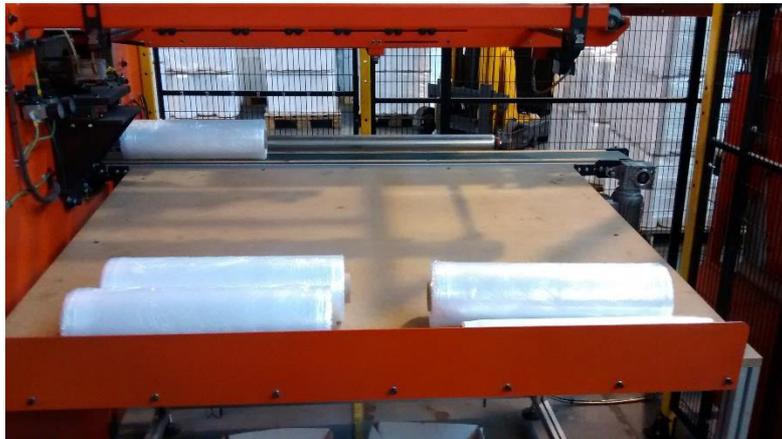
Buffer de produto acabado à saída de uma máquina "Laranja"
